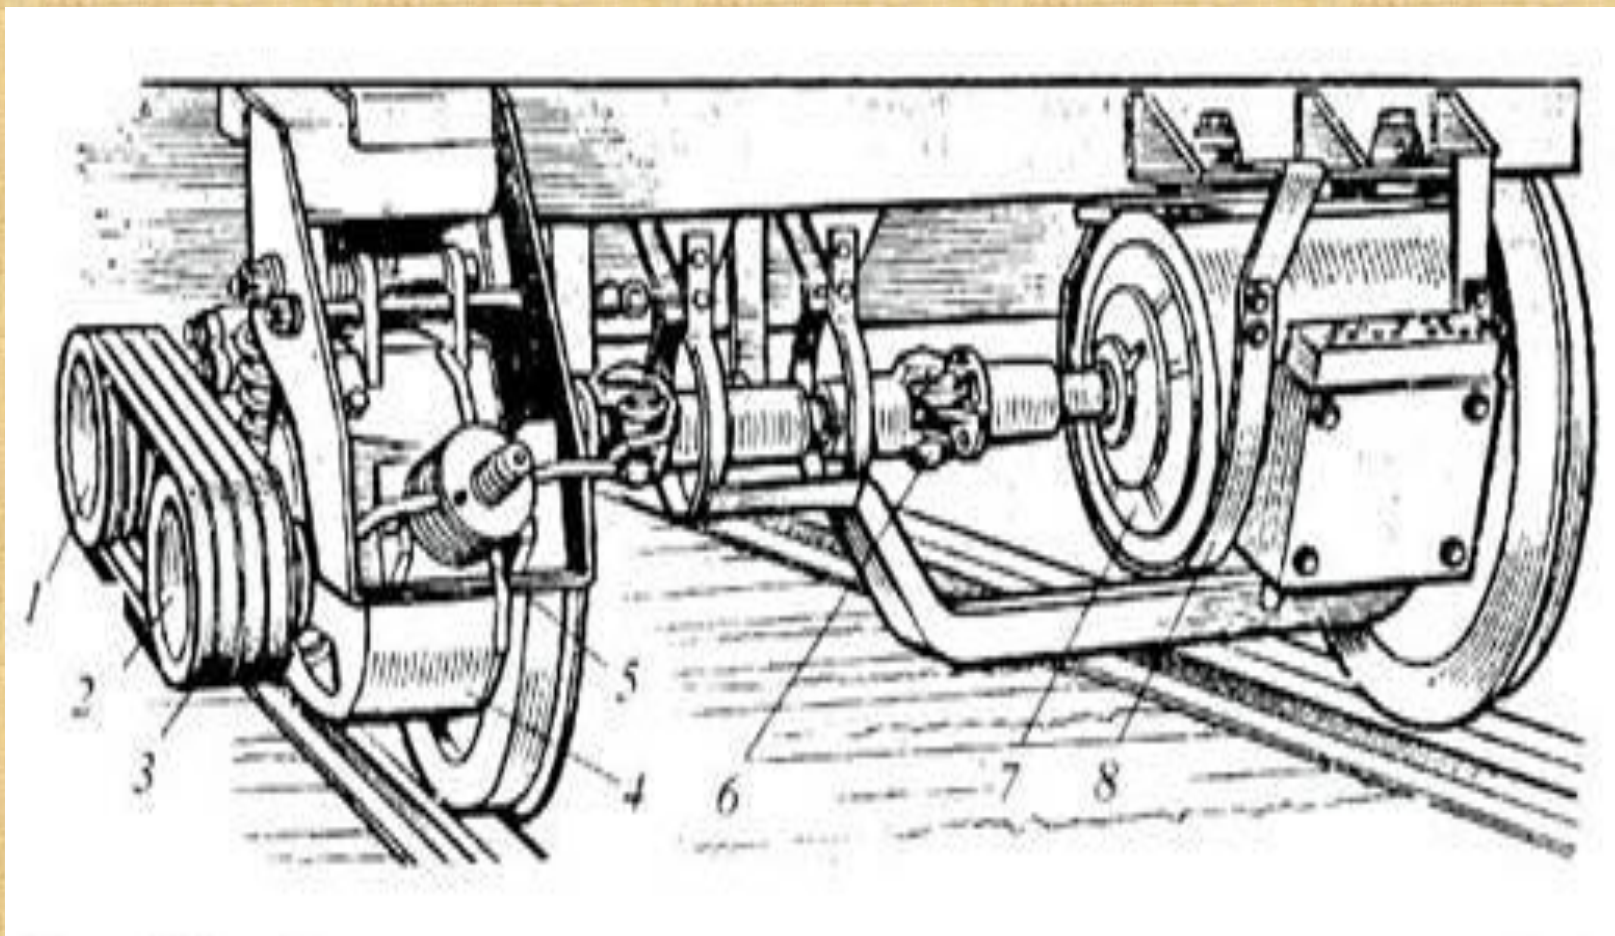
Расположение клиноременного привода генератора: 1 – ведущий шкив; 2 – ведомый шкив; 3 – четыре приводных клиновых ремня; 4 – редуктор; 5 – натяжное устройство; 6 – карданный вал; 7 – генератор; 8 – предохранительные устройства вала и генератора.
